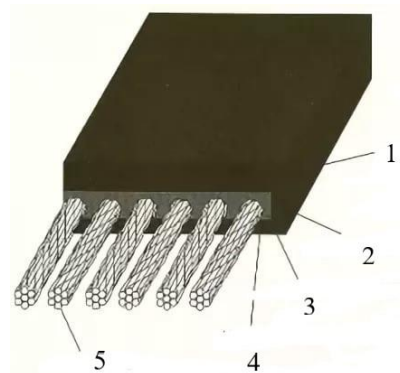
Резинокордовая лента: 1 – рабочая обкладка, 2- резиновый борт, 3- резина каркаса, 4 – нерабочая обкладка, 5 – стальные тросики
